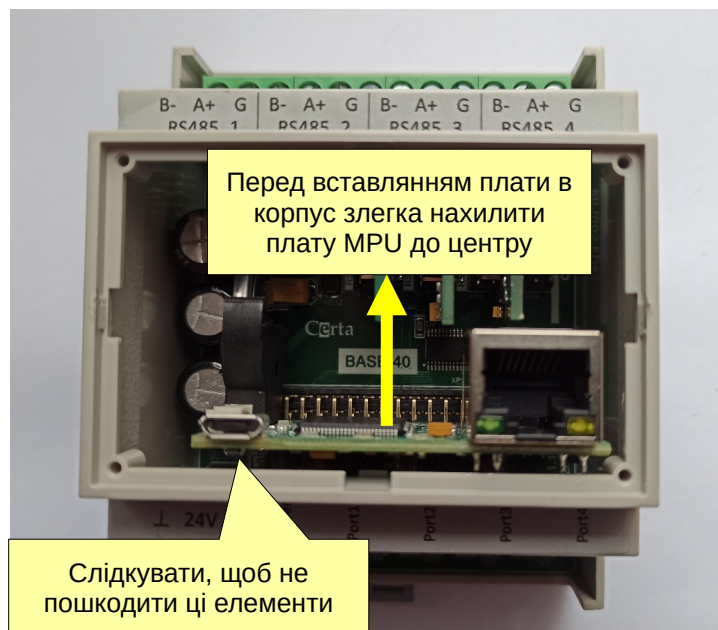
Встановлення плати BASE в корпус (вид згори)
